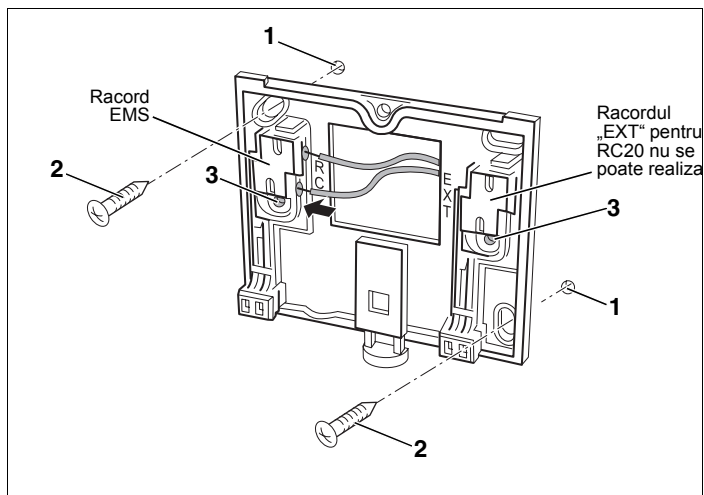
Fixarea plăcii de montaj pe tencuiala
